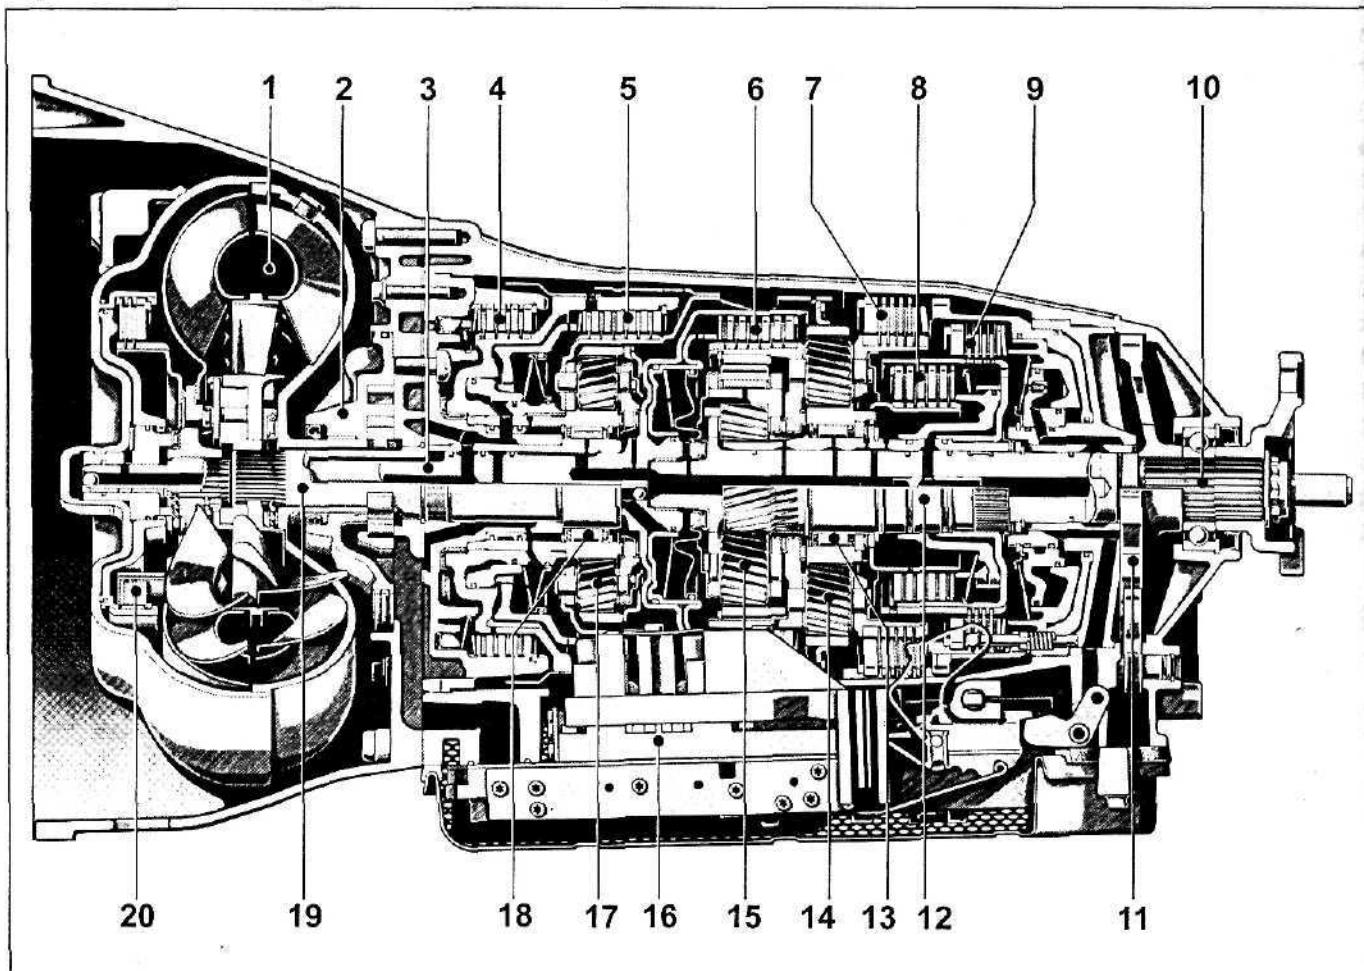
1- гидротрансформатор; 2 - масляный насос; 3 - ведущий вал; 4 - дисковый тормоз В1; 5 - блокировочная муфта К1; 6 - блокировочная муфта К2; 7 - дисковый тормоз В3; 8 - блокировочная муфта К3; 9 - дисковый тормоз В2; 10 - ведомый вал; 11 - шестерня механизма блокировки выходного вала; 12 - промежуточный вал; 13 - муфта свободного хода F2; 14 - задний планетарный ряд; 15 - средний планетарный ряд; 16 - электрогидравлический блок управления; 17 - передний планетарный ряд; 18 - муфта свободного хода F1; 19 - вал реактора гидротрансформатора; 20 - муфта блокировки гидротрансформатора.
